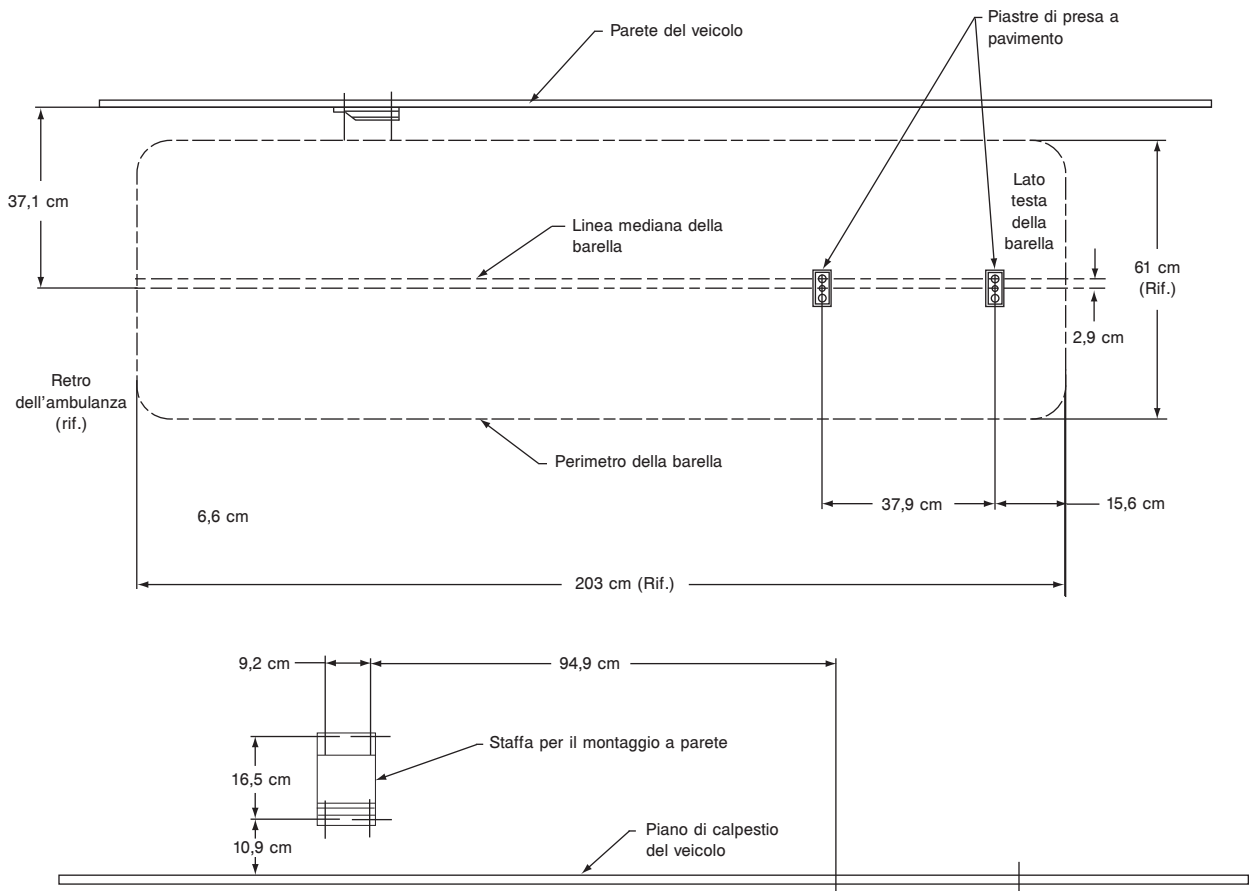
Dati tecnici di installazione – Sistema di ancoraggio a parete
